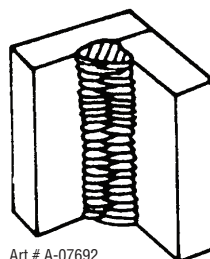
Position verticale, Soudure d'angle
